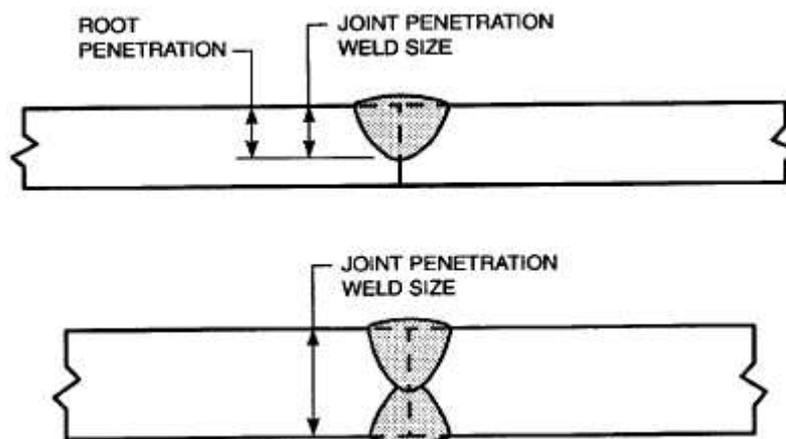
Tamaños de soldadura de ranura con juntas de penetración parcial y completa.
